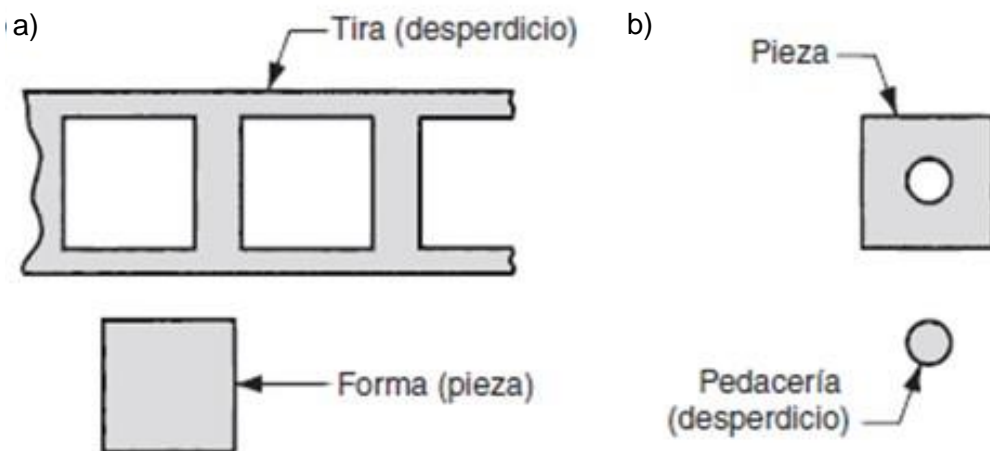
Operaciones de corte: a) Punzonado; y b) perforado [1].
